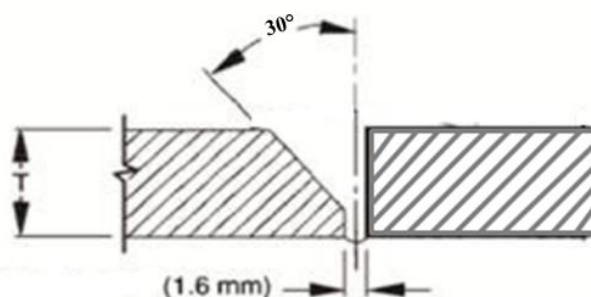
Esquema do chanfro da junta JM em corte transversal.
